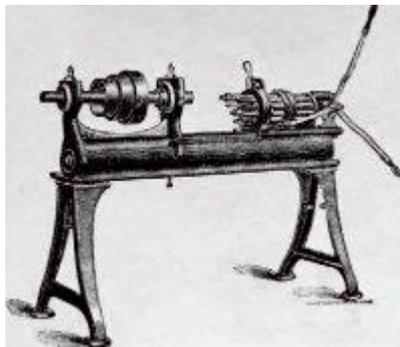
Primer torno desarrollado. Imagen tomada del museo de la maquina herramienta.
